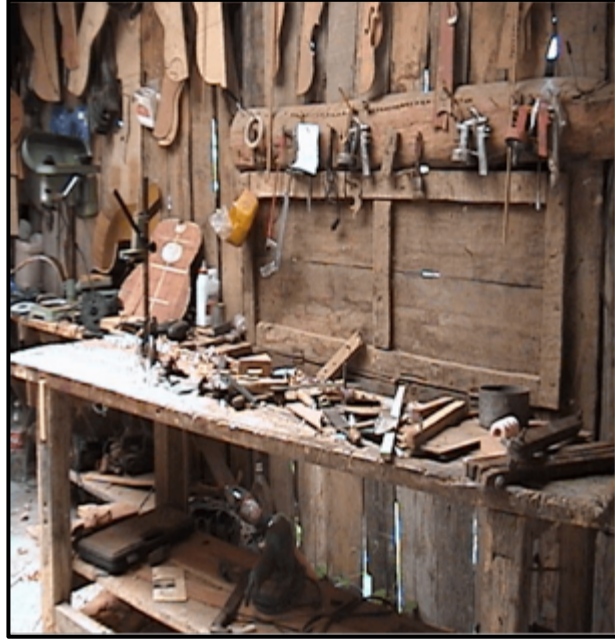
Banco de trabajo en El Desdavi, con plantillas de huapanguera, jarana huasteca, y violín. Foto J. L. Sagredo
